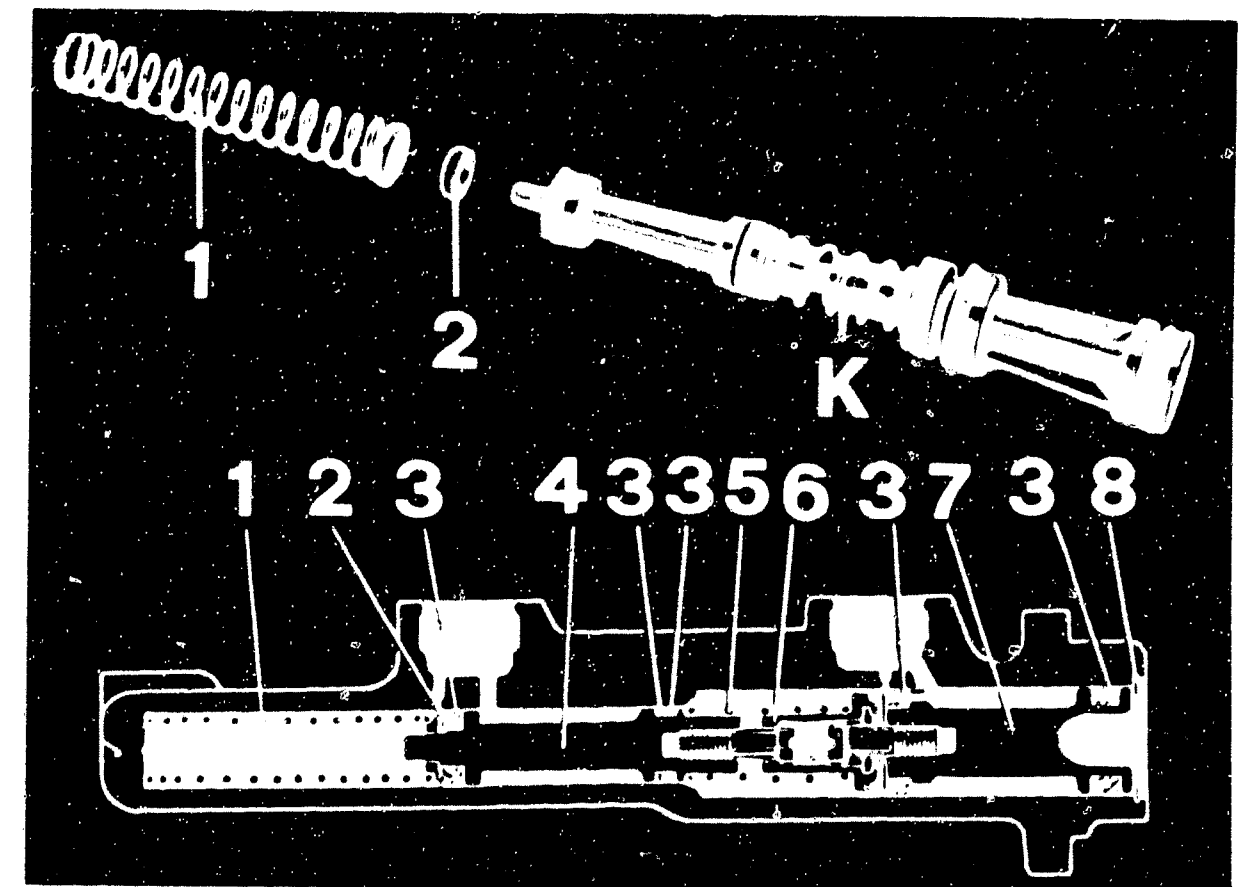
oben: Druckfeder (1), Federteller (2) und zusammengebauter Kolben (K) des Hauptbremszylinders. Unten: Schnittbild durch den Hauptbremszylinder: 1 Druckfeder – 2 Federteller – 3 Kolbendichtung – 4 Sekundärkolben – 5 Rückholfeder – 6 Fesselhülse – 7 Primärkolben – 8 Sicherungsring.
